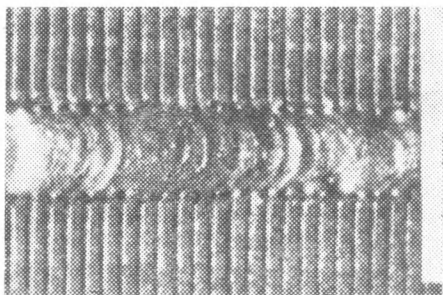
Лазерная сварка листового пакета из муниперма (Muniperm) (CO_2 -лазер, 120 Вт, непрерывное излучение)
